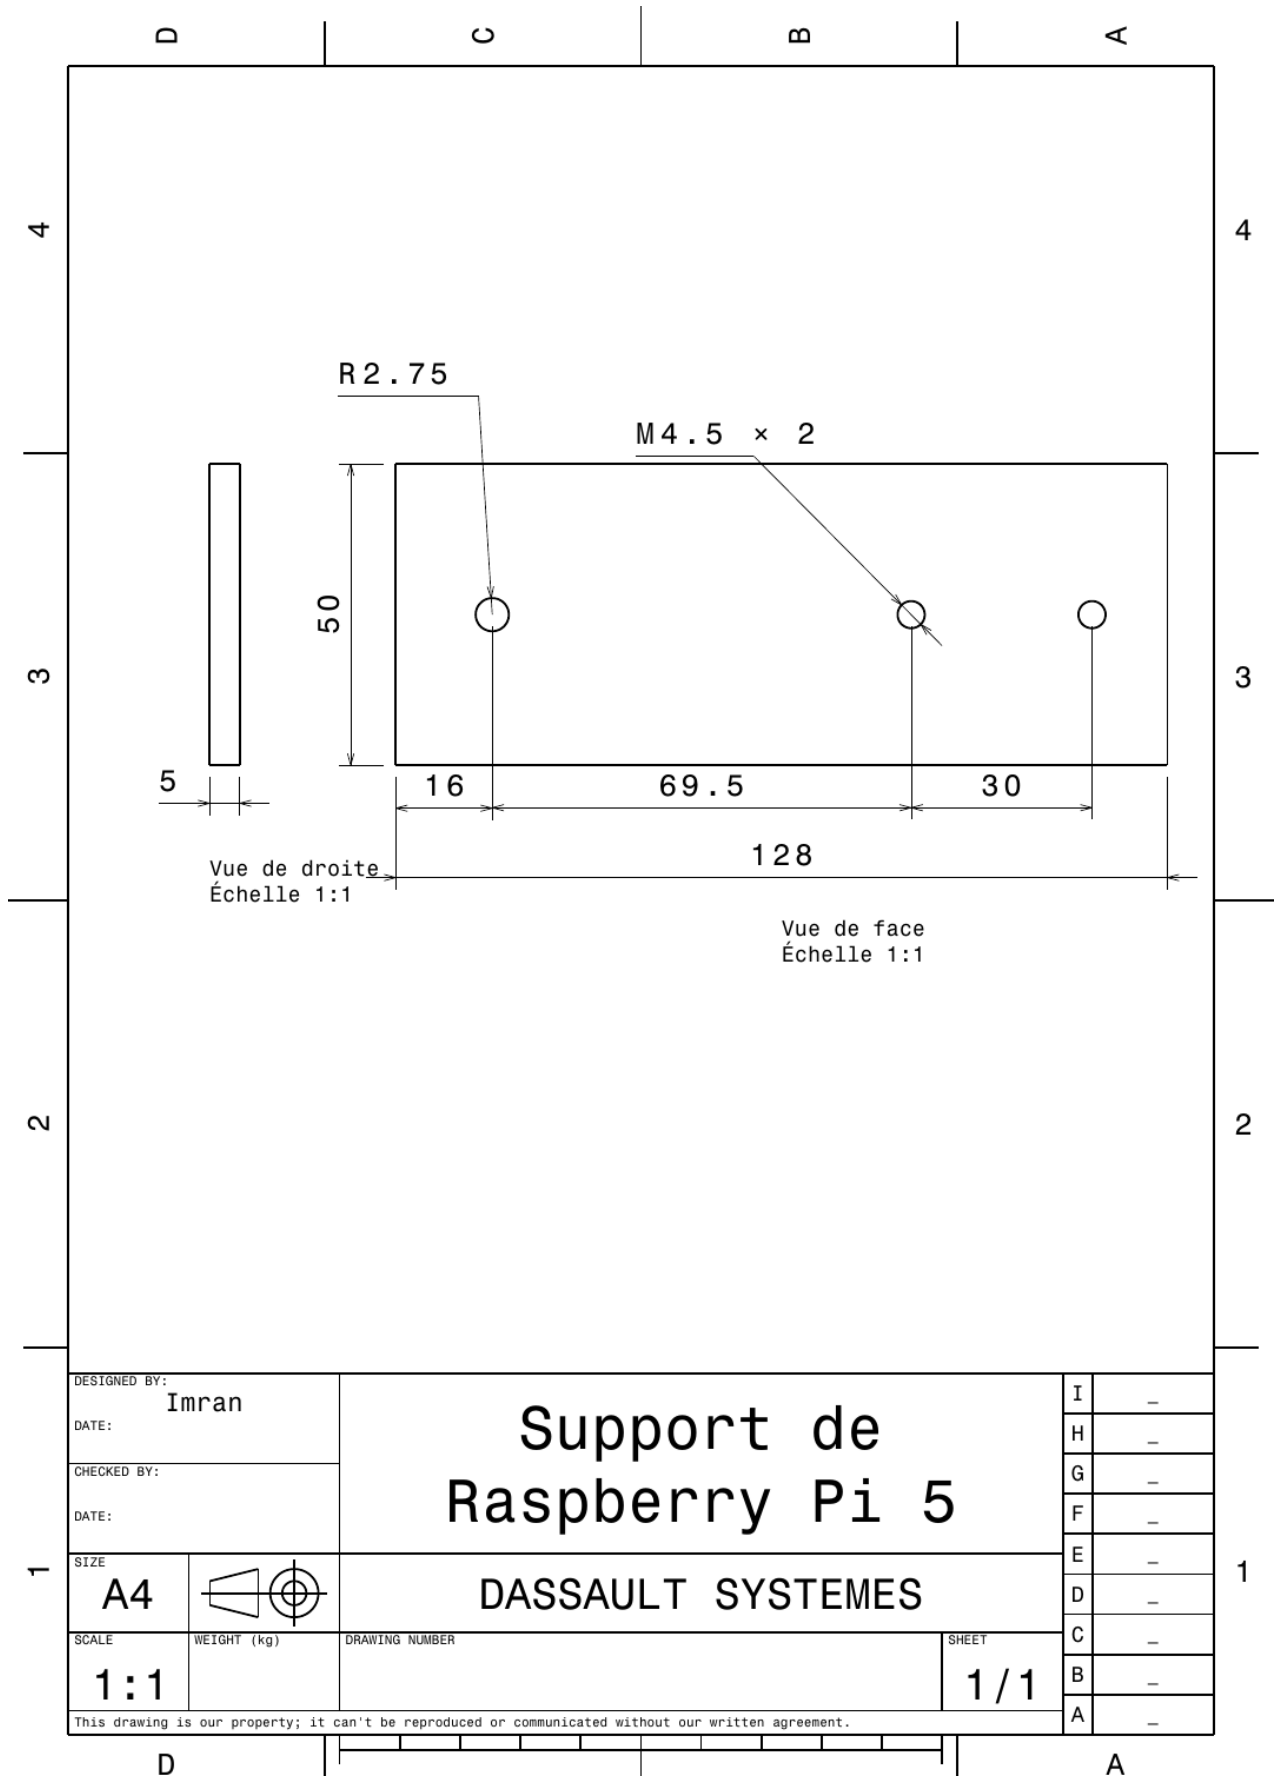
Dessin de définition — Support du Raspberry Pi 5.
